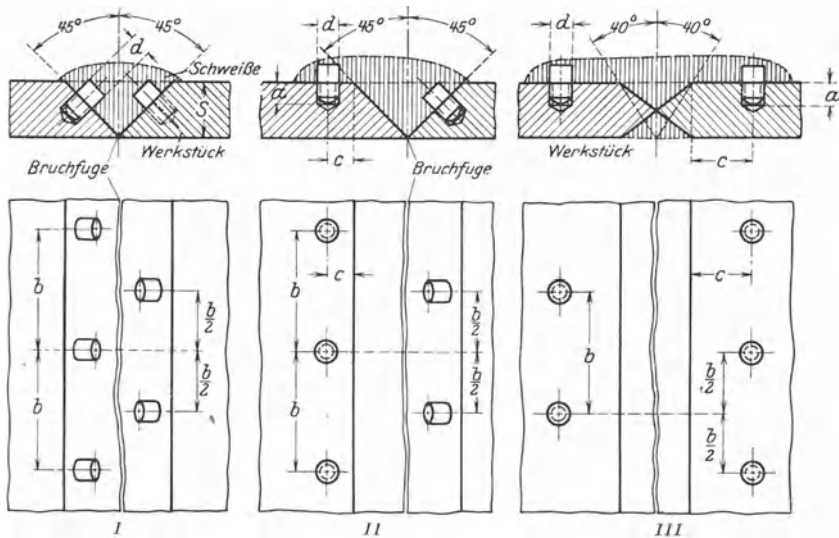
Anordnung von Stiften bei Gußeisenkalterschweißungen.
